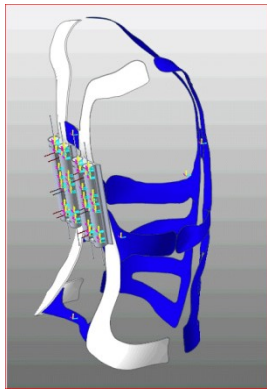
CAD Zeichnung eines CareJack Prototypen
